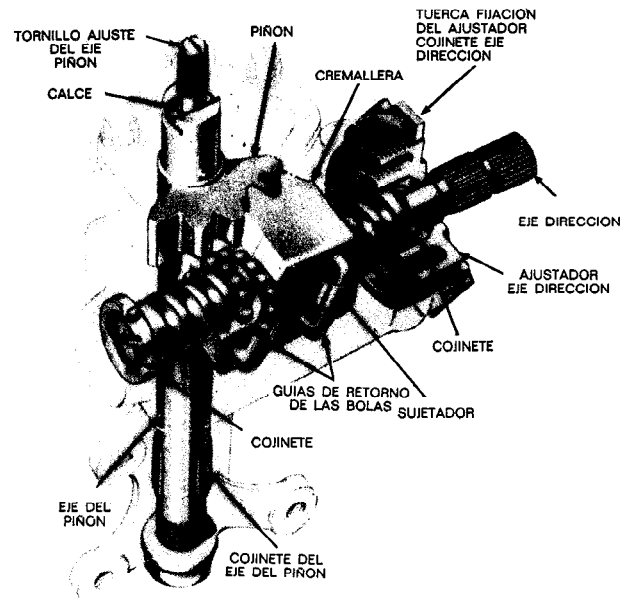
Dirección del tipo de bolas circulantes (Ford Motor Company).
